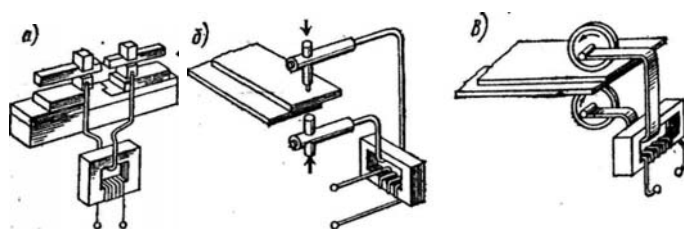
Схема различных видов контактной сварки
